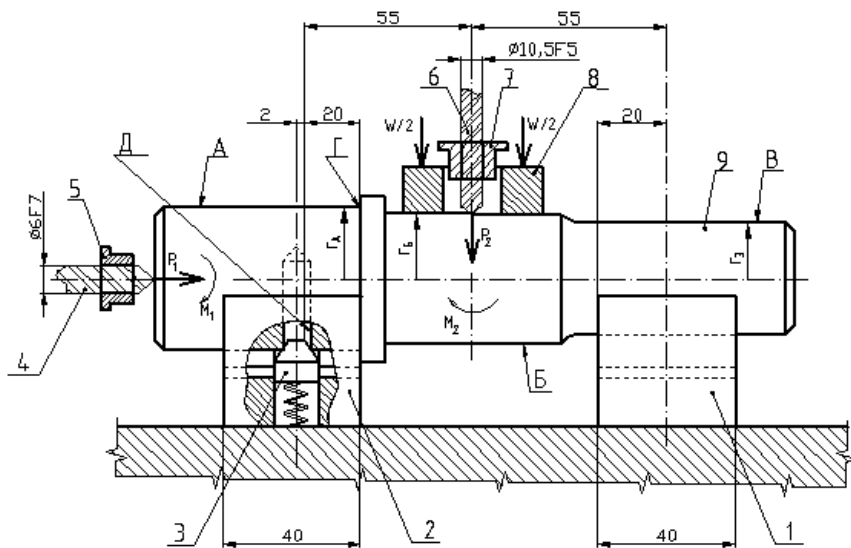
Схема базирования, закрепления и обработки заготовки
